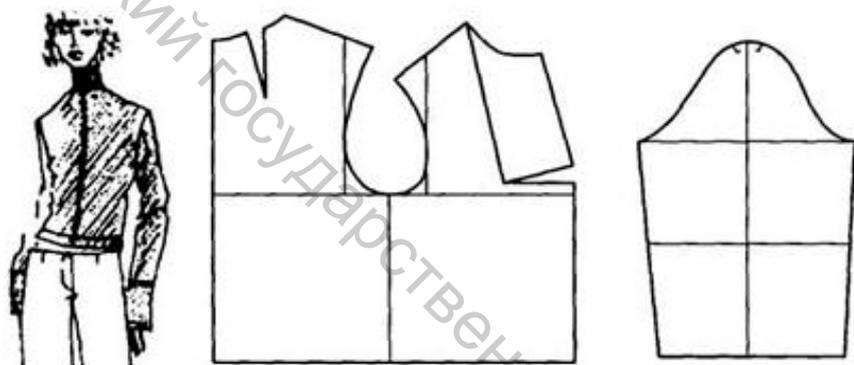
Схема конструкции изделия с втачными рукавами
